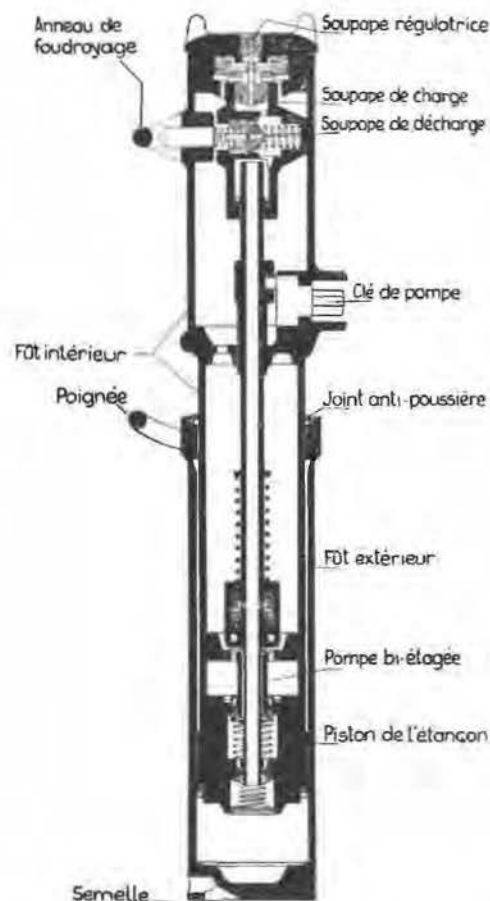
Coupe de l'étauçon hydraulique Eisenwerk-Wanheim.
